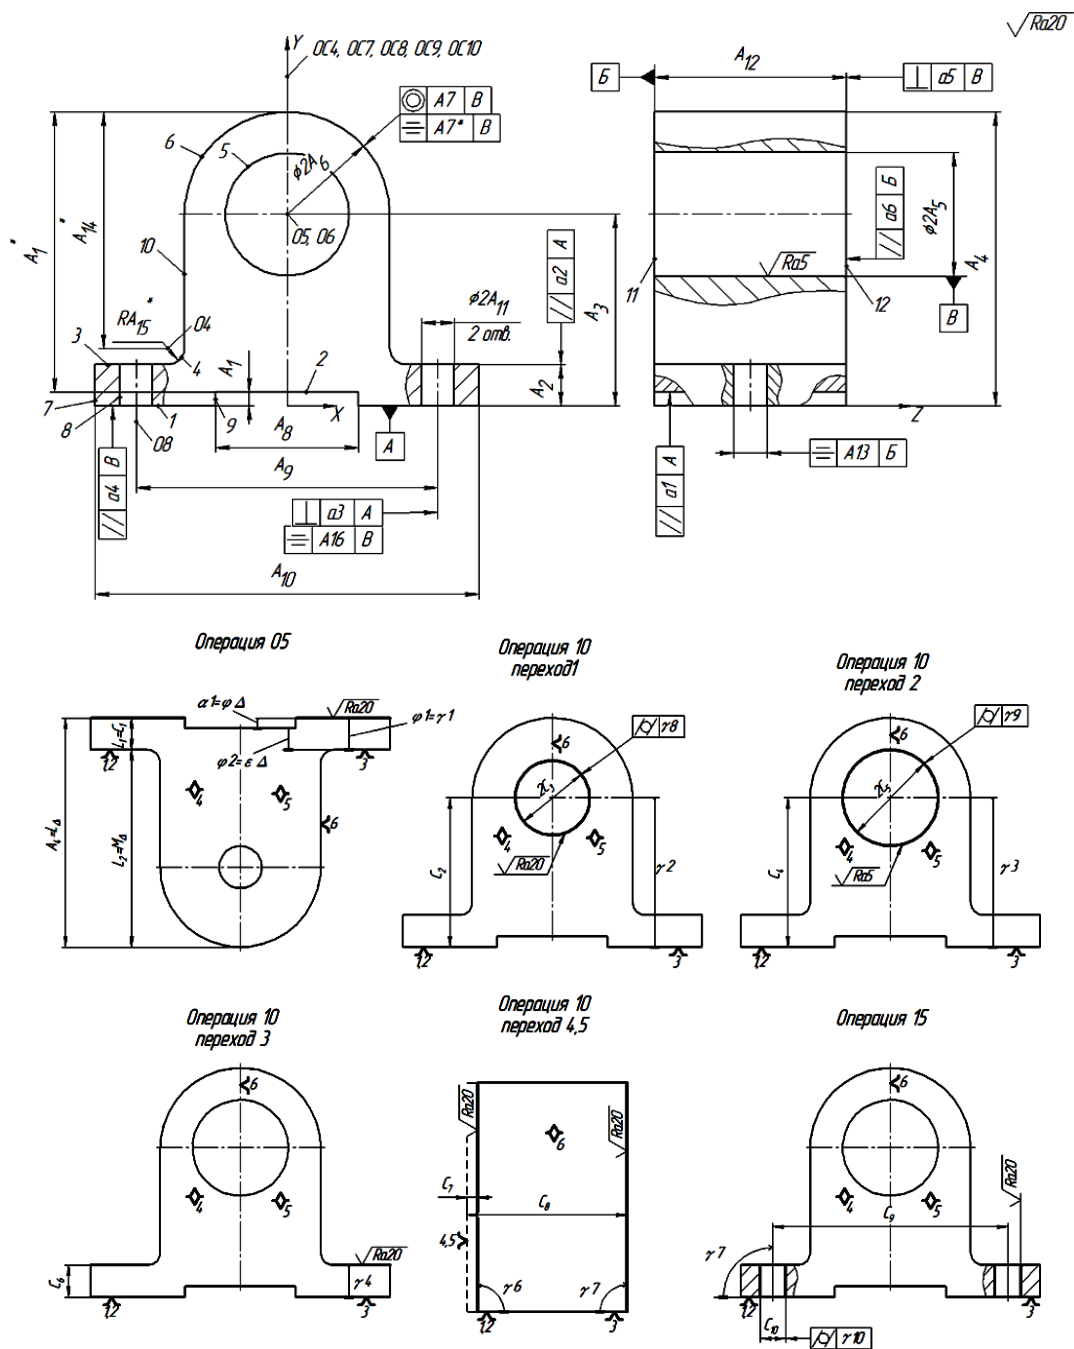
Чертеж детали «корпус» и операционные эскизы ее обработки
